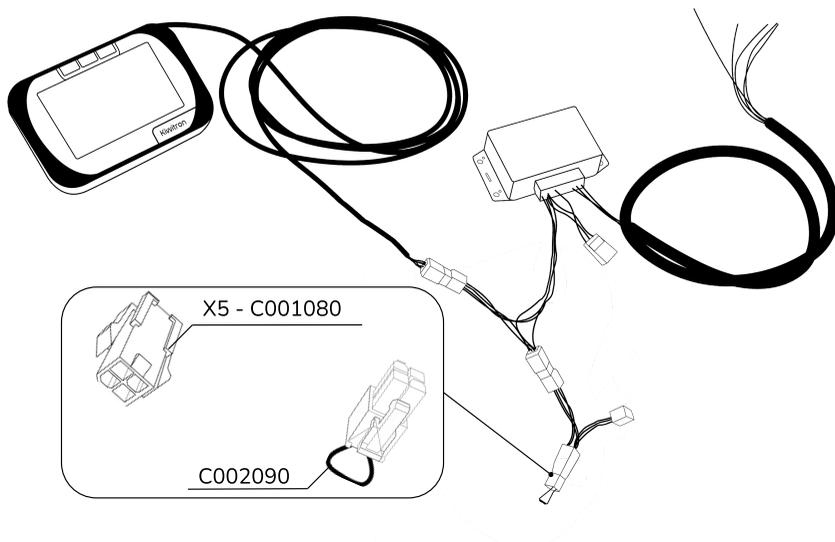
Collegamento terminazione X4 (chiusura CAN)
